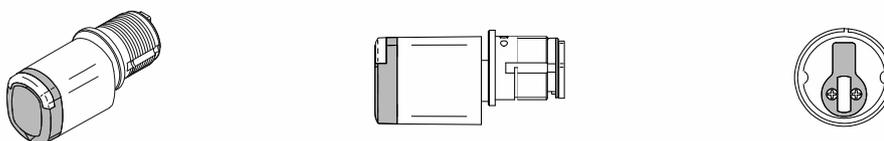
Профиль Mortise. Полуцилиндр со считывающей головкой
